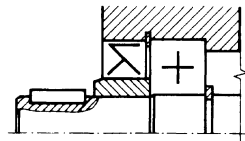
Radial-Wellendichtring mit Staublippe (mit Wälzlager)
